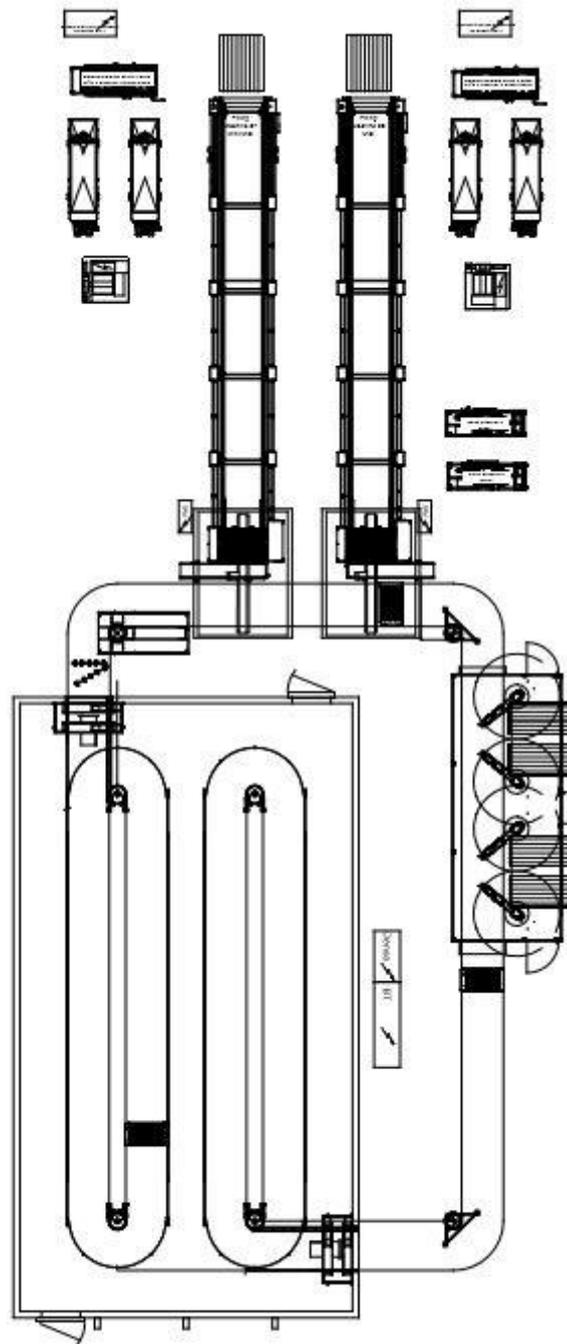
Vista en planta de la zona húmeda de la línea CONO-MIDI
